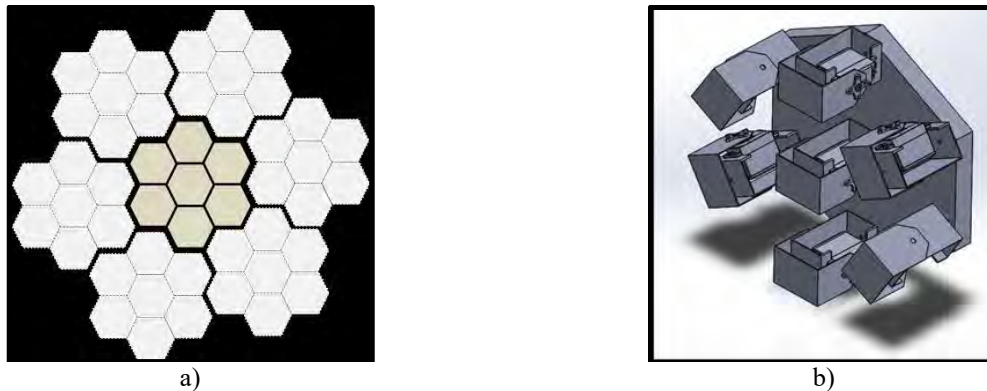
Diseño de sistema modular servo-controlado de siete espejos. a) Celda hexagonal básica. b) Diseño en solidworks.
